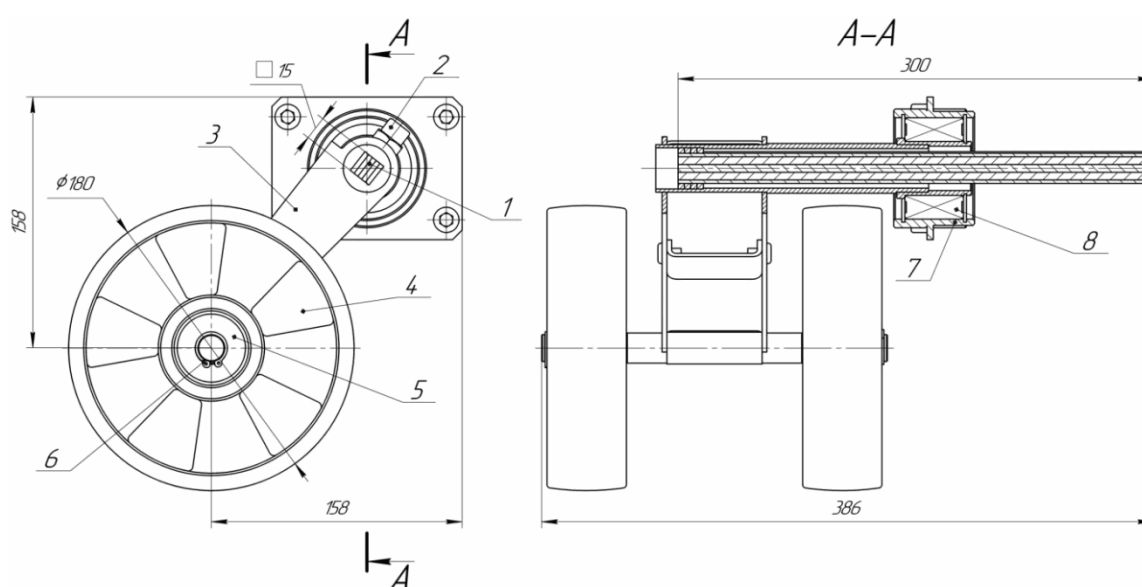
Узел подвески платформы «Объект 314»: 1 – торсион; 2 – стопорный винт; 3 – балансир; 4 – колесо; 5 – подшипник колеса; 6 – кольцо стопорное; 7 – корпус подшипника балансира; 8 – подшипник балансира
